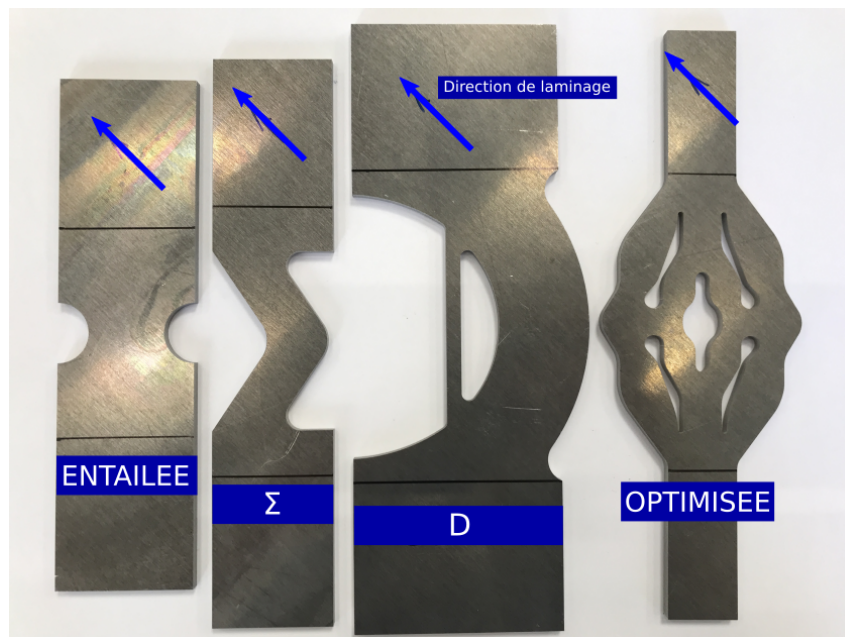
Photographies des éprouvettes testées avant essai.
